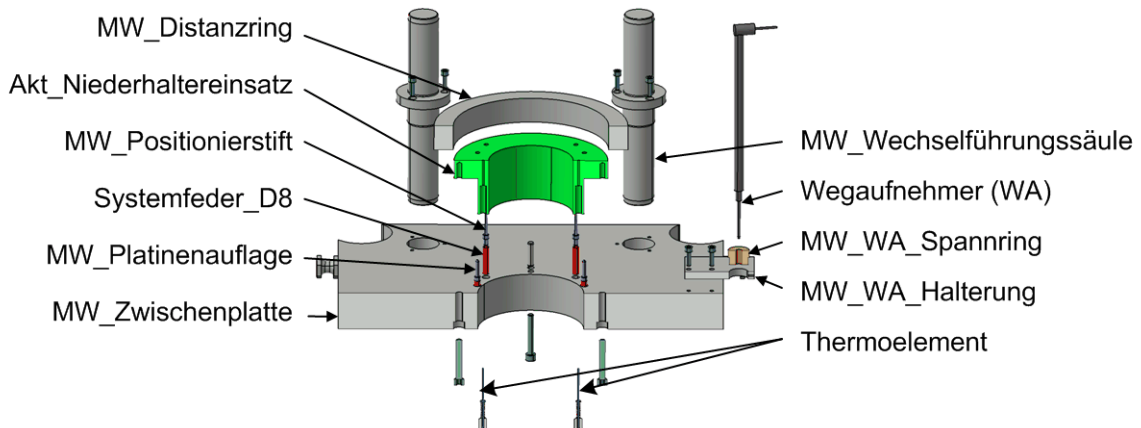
Mittleres Werkzeug (MW) des Halbwarmschneidwerkzeugs
